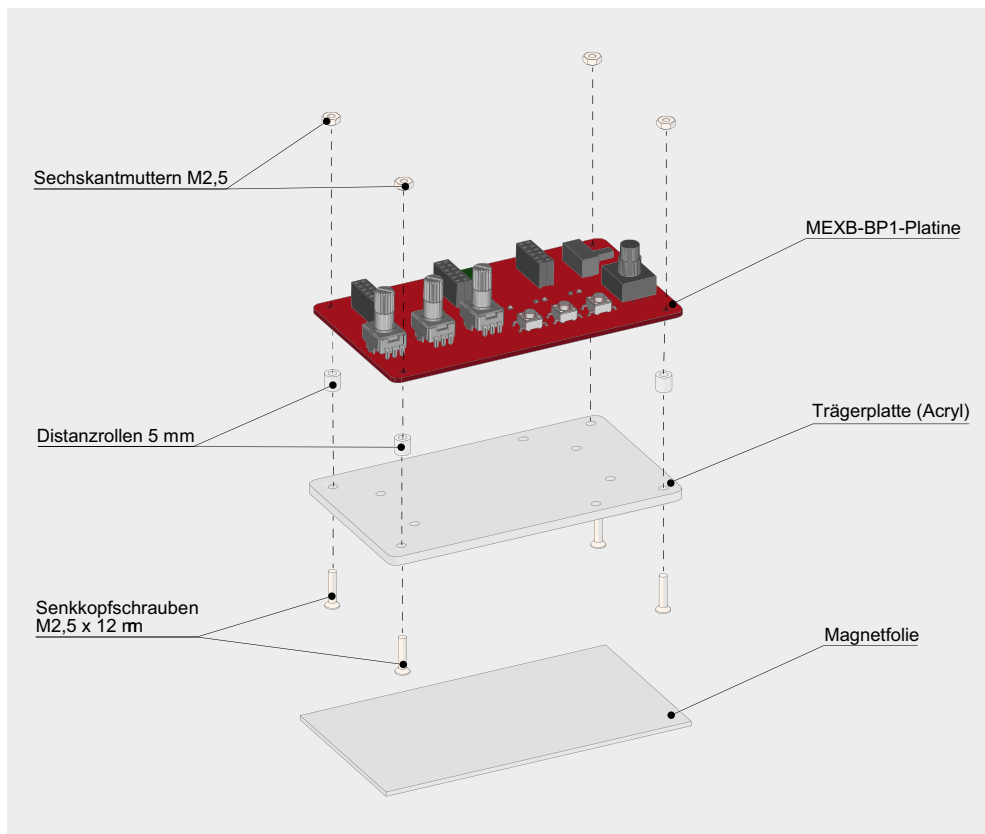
Explosionszeichnung für die Montage auf der Trägerplatte
